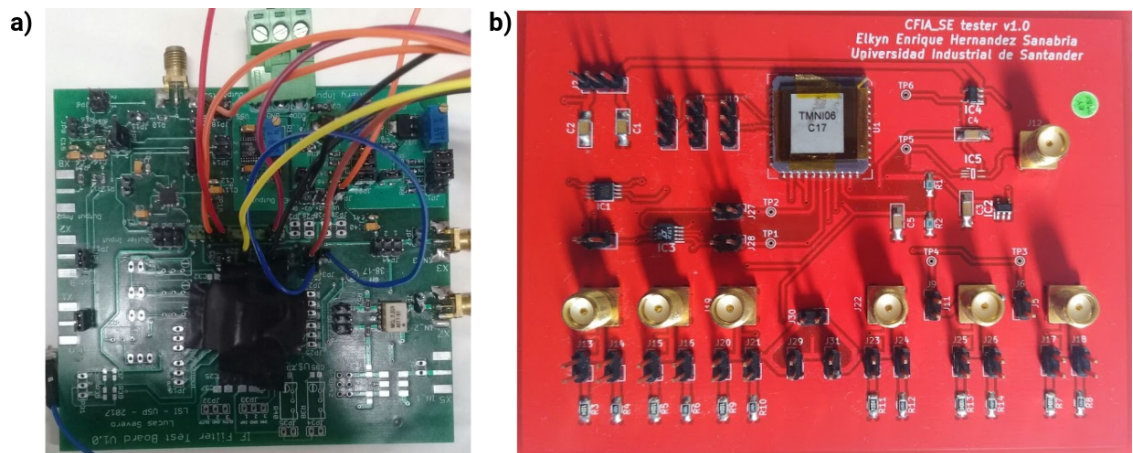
a) PCB de pruebas del chip multiproyecto desarrollado por el LSI-USP. b) PCB de pruebas dedicada para el CFIA.
